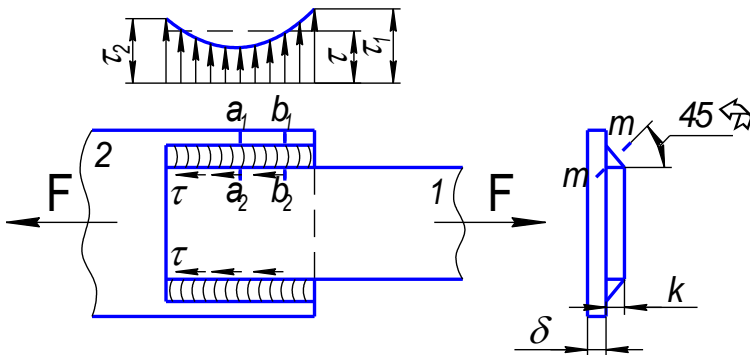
Розрахункова схема для розрахунку флангового зварного з'єднання
